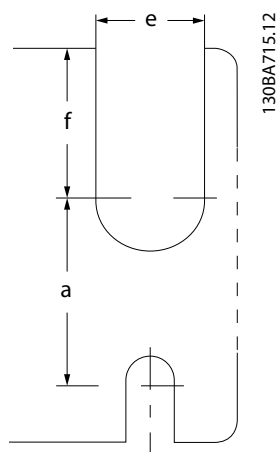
Pravilna montaža z zadnjo ploščo
